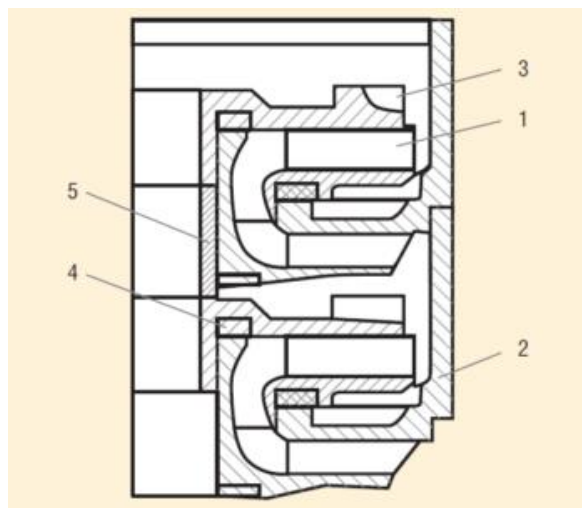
Ступень двухопорной конструкции из серого чугуна
